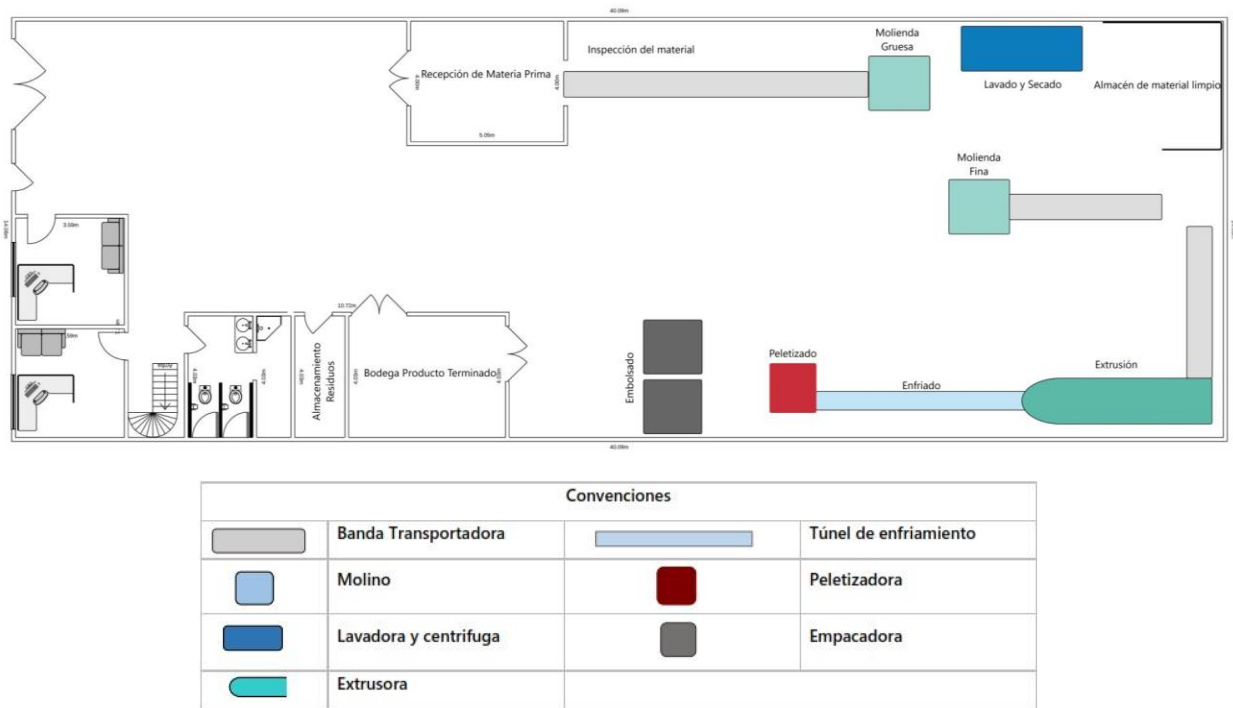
Distribución de la planta 1, Planta de tratamiento de plástico PET, PEBD Y PEAD
